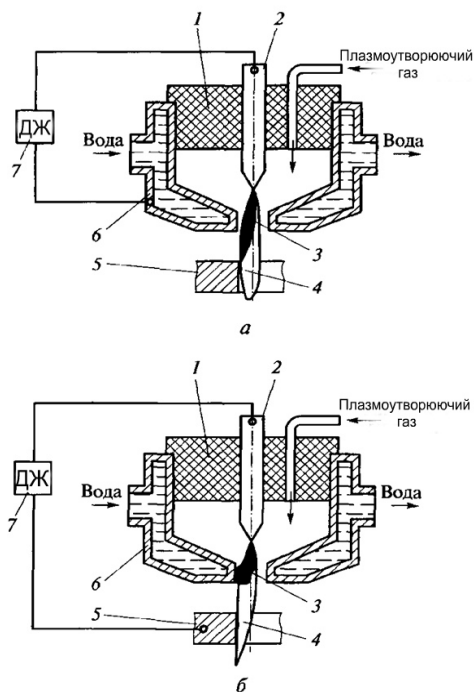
Схеми зварювання незалежним плазмовим струменем (а) та плазмово-дугового зварювання (б):
